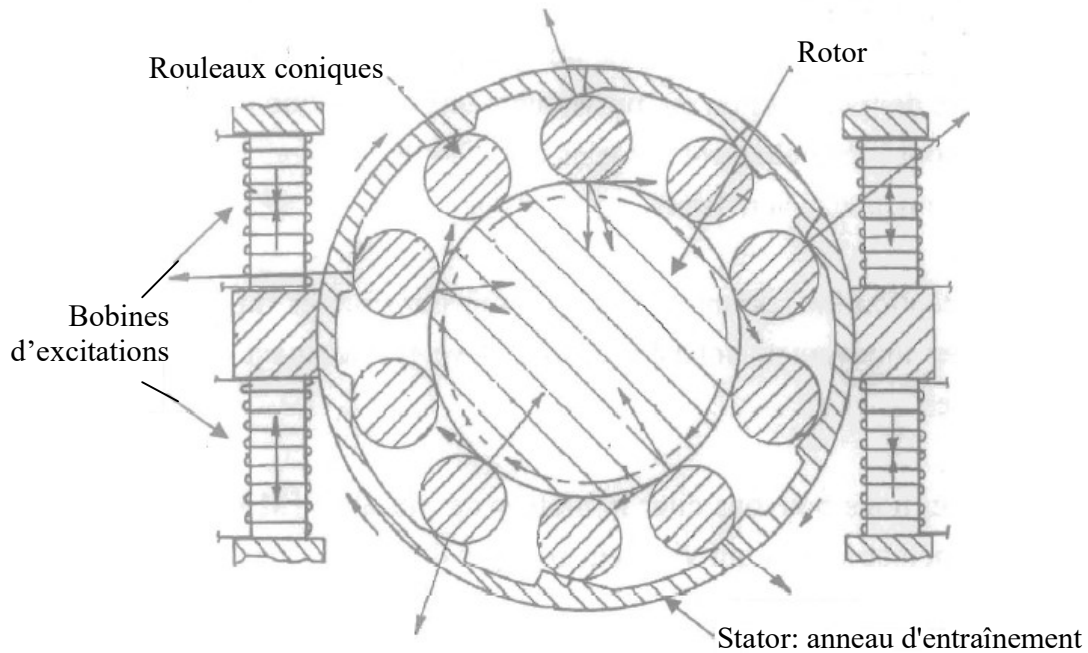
Moteur de Vranish , brevet déposé par la NASA - vue en coupe de dessus –
